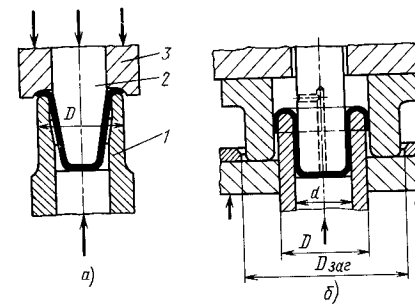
Схемы конструкций штампов для выворотной (реверсивной) вытяжки
